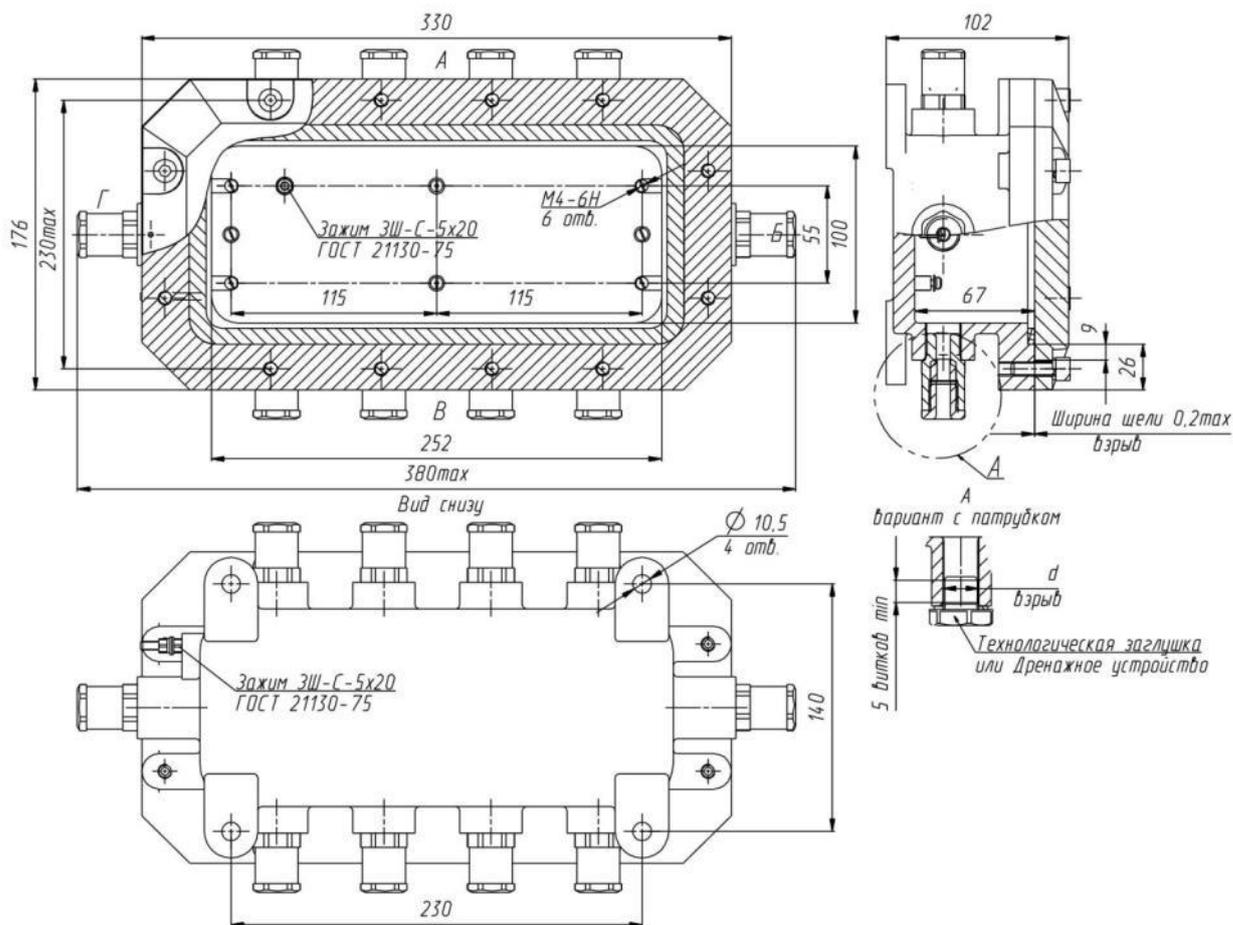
Общий вид и габаритные размеры коробки ЕхКК-А1
